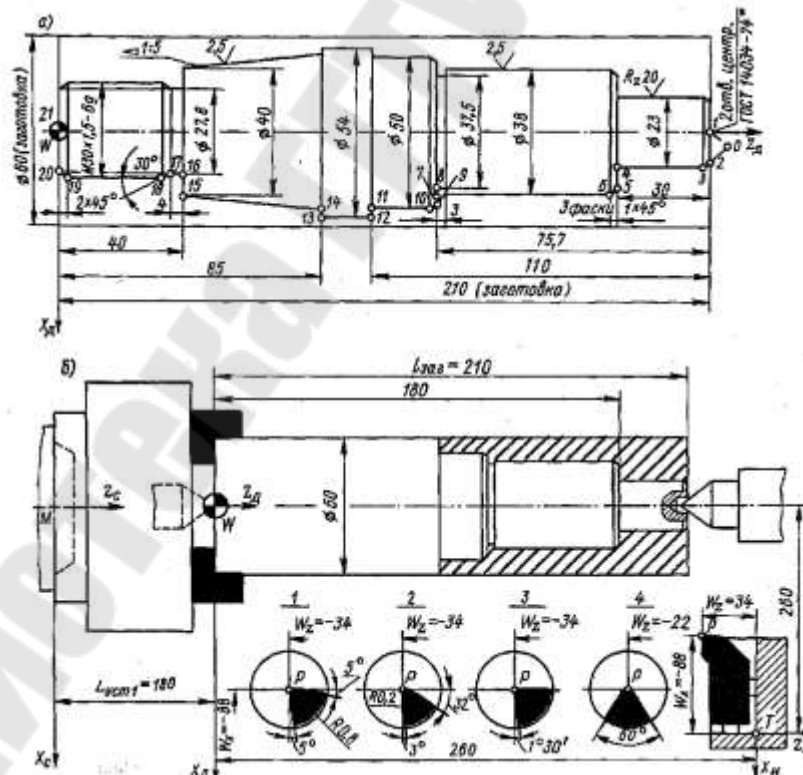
Совмещенные элементы РТК (а – чертеж детали в системе координат детали) и карты наладки (б – общая схема установа детали на станке) токарного станка с ЧПУ
